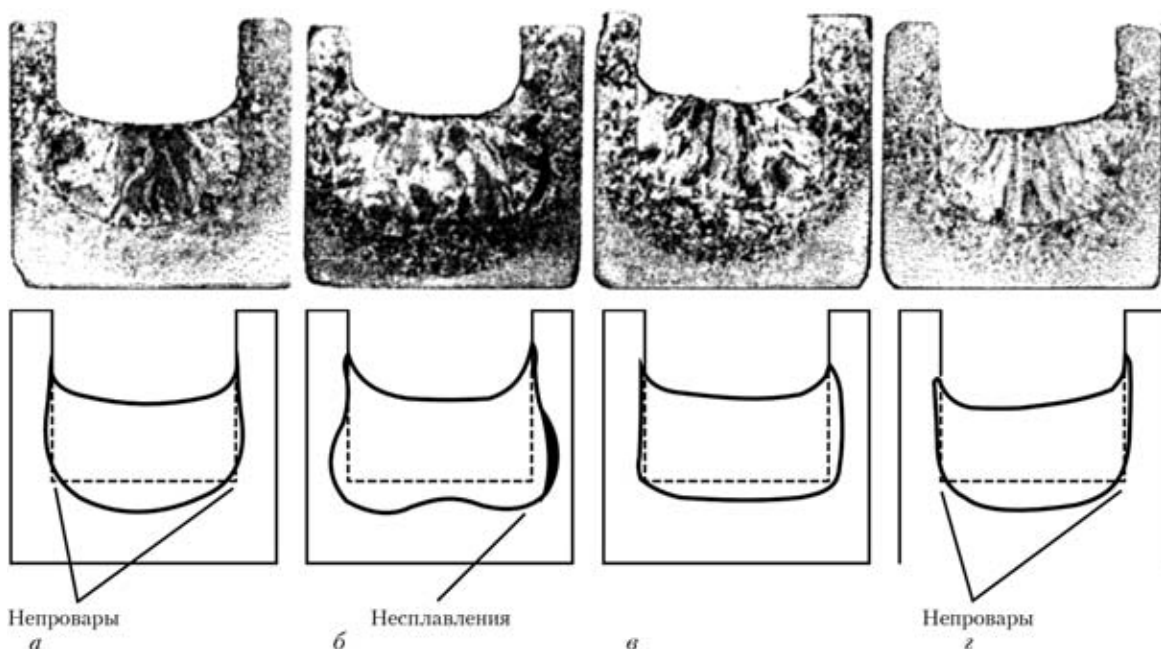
Макрошлифы валиков, полученных сваркой в узкий зазор (вверху), и схемы форм проваров (внизу): а — валик, полученный без управляющего магнитного поля; б —  $b_в < b_н$ ; в —  $b_в = b_н$ ; г —  $b_в > b_н$
